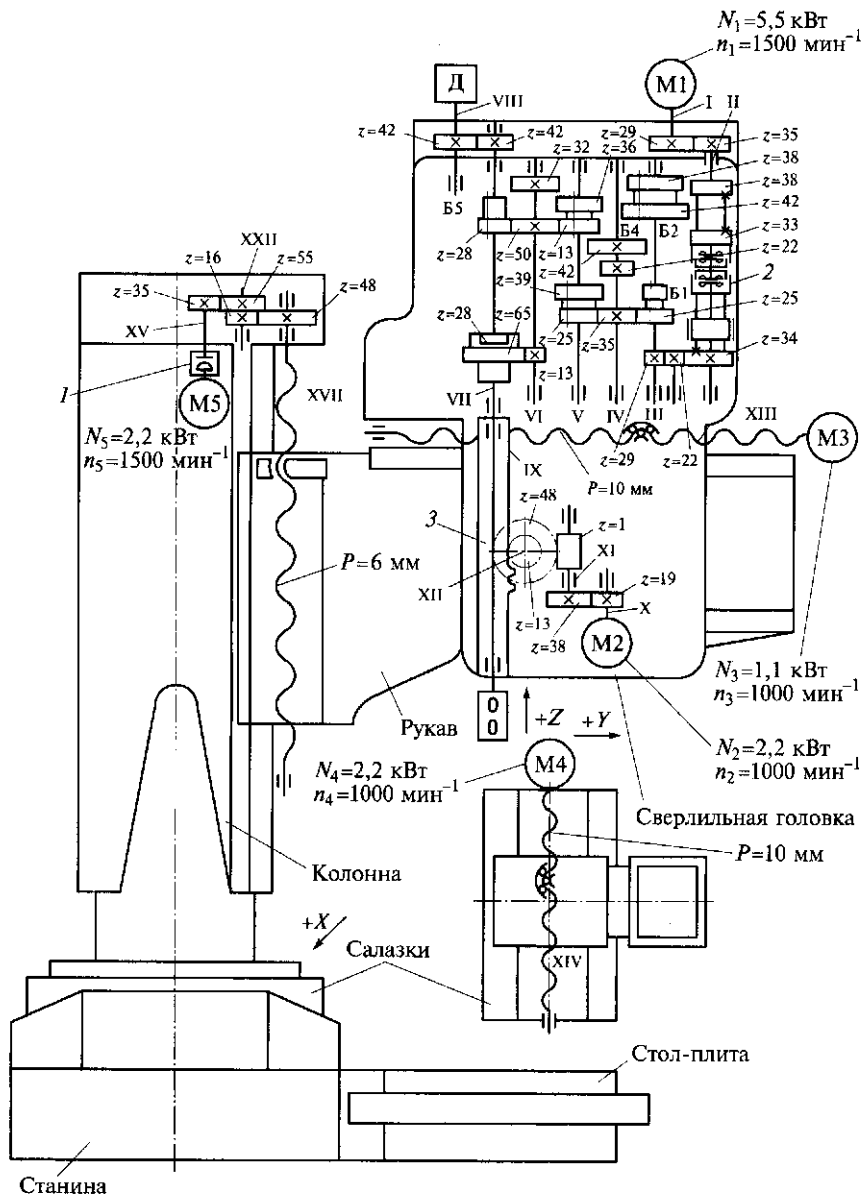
Кинематическая схема радиально-сверлильного станка с ЧПУ: 1, 2 — муфты; 3 — рейка ( $m = 3 \text{ мм}$ ); М1 — М4 — электродвигатели; Б1 — Б5 — двойные блоки зубчатых колес коробки скоростей; Д — датчик нарезания резьбы
